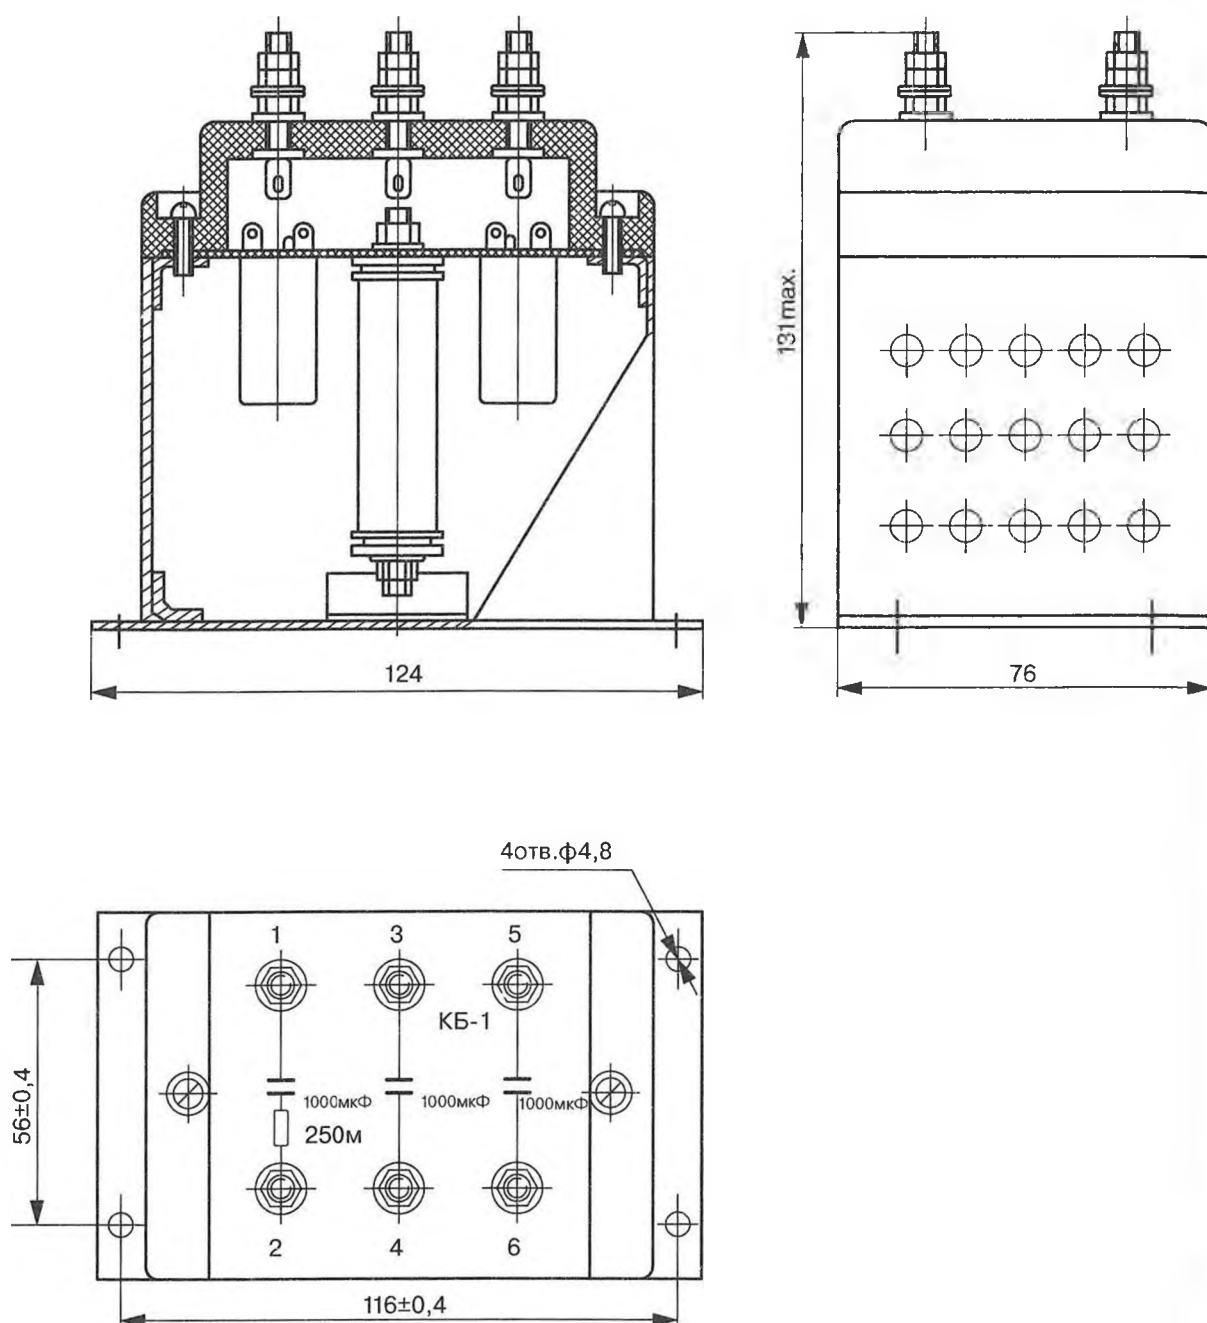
Габаритные и установочные размеры блока конденсаторного КБ-1
